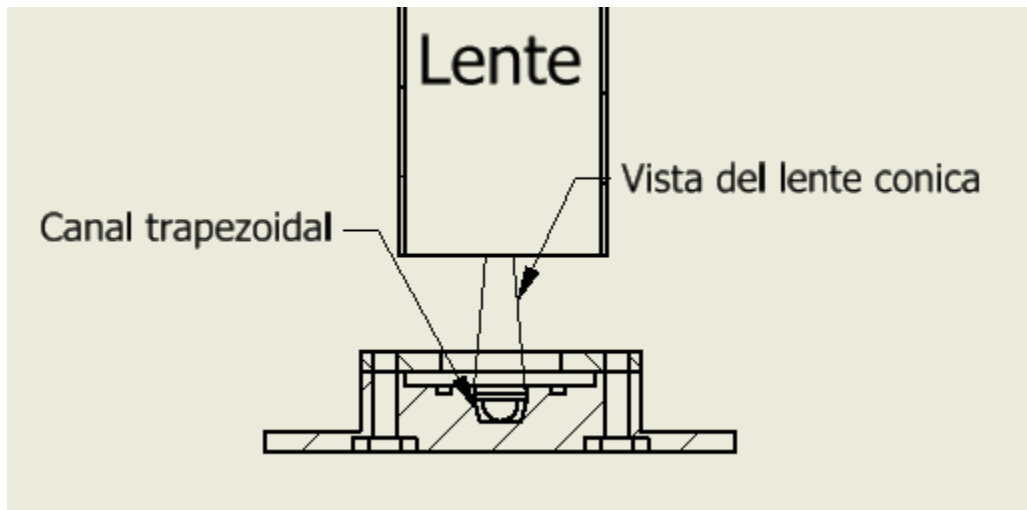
Sección transversal del sistema de inspección. (Elaboración propia)
